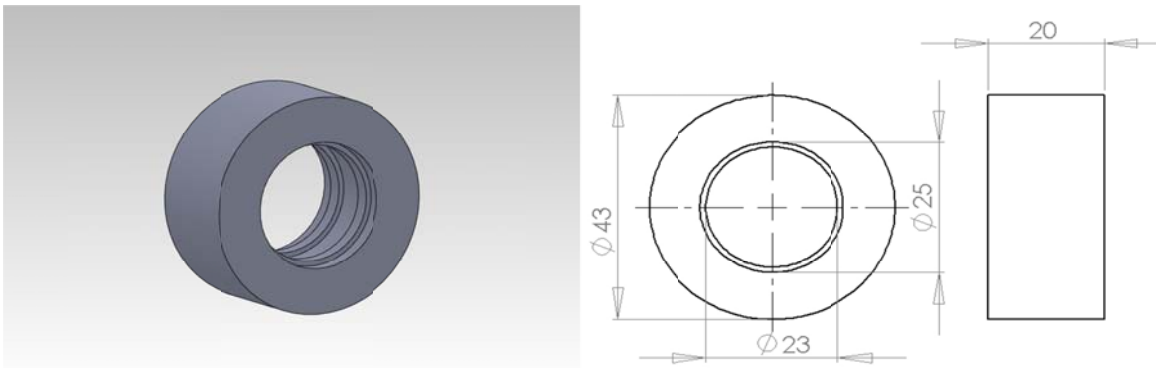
Dibujo CAD de la llanta utilizada.
